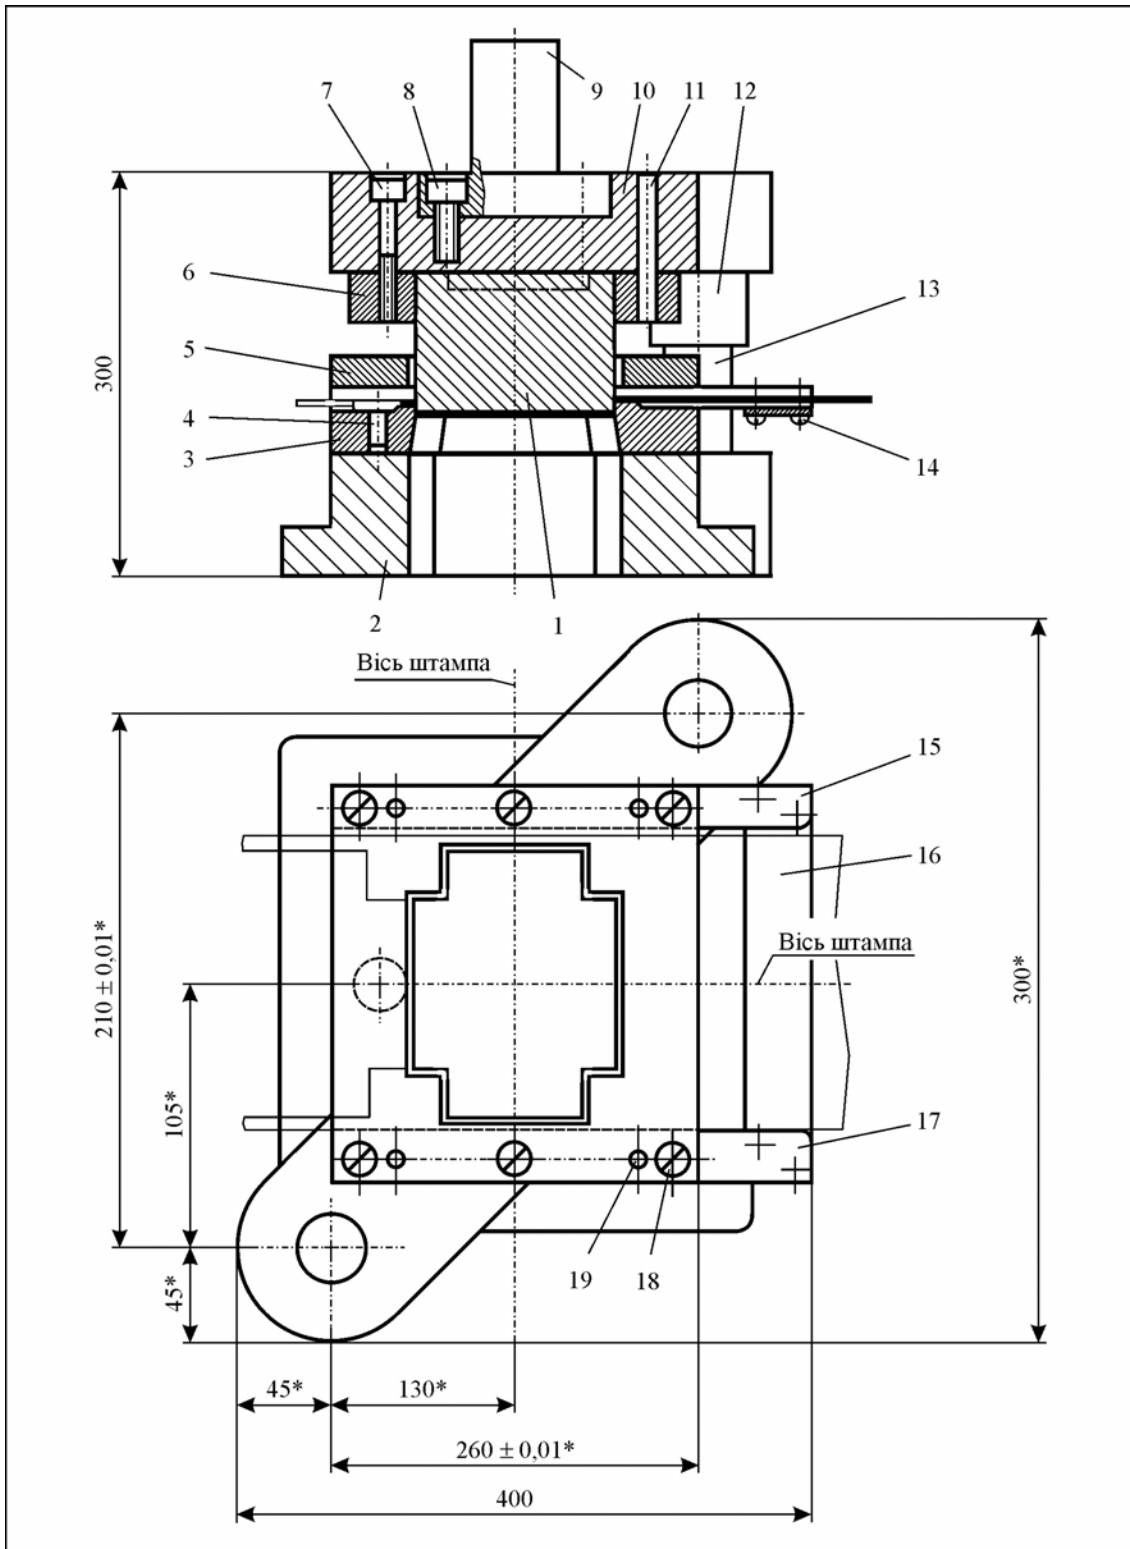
Штамп для вирубівання малогабаритної деталі: 1 – пуансон; 2 – нижня плита; 3 – матриця; 4 передній упор; 5 – жорсткий знімач; 6 – пуансонотрмач; 7, 8, 14, 18 – гвинти; 9 – хвостовик; 10 – верхня плита; 11, 19 – штифти; 12 – втулка; 13 – колонка; 15, 17 – напрямні планки; 16 – опорна планка
